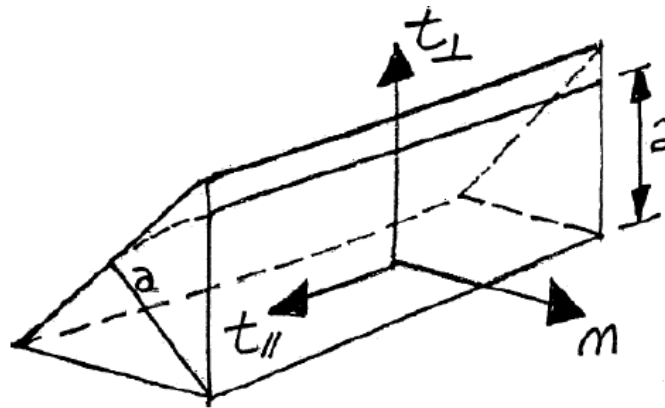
Representação das tensões no cordão de soldadura. (Castro, 2013)
